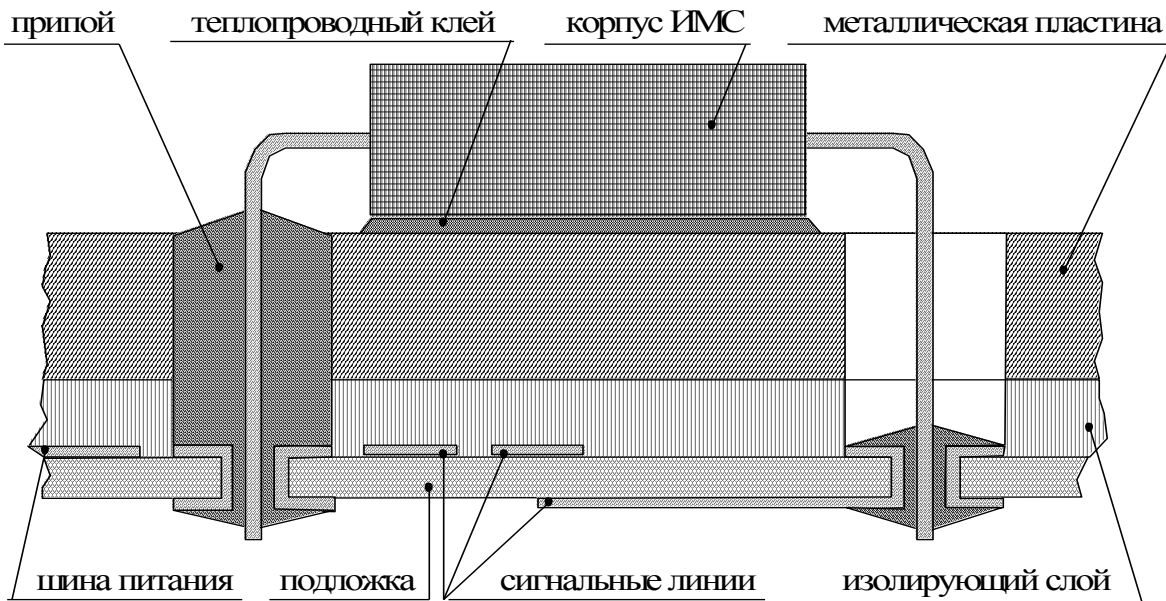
Конструкция помехозащищённой теплопроводной монтажной платы
